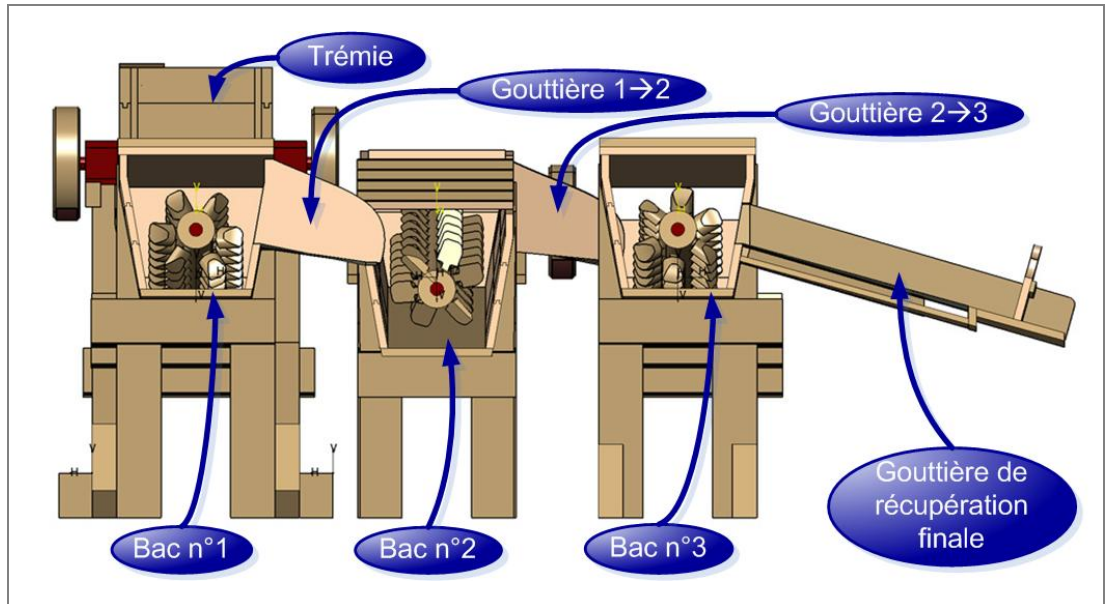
MAQUETTE CAO, VUE ARRIERE EN COUPE DES 3 BACS
